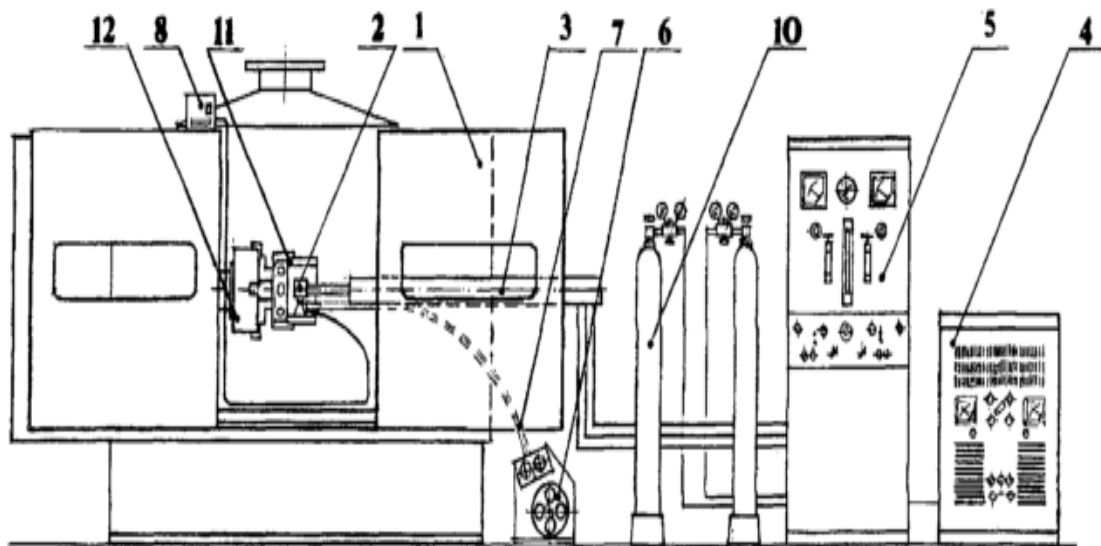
Установка для механізованого напilenня внутрішніх поверхонь.
